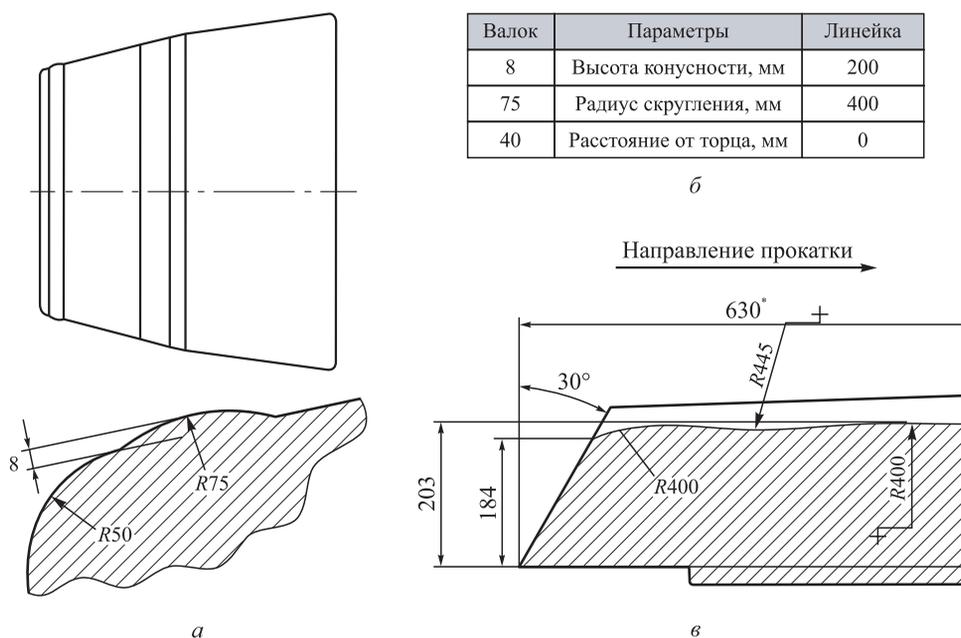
Параметры гребня на валке и линейки: чертеж валка с гребнем (а); основные параметры (б); чертеж линейки с конусностью (в)
